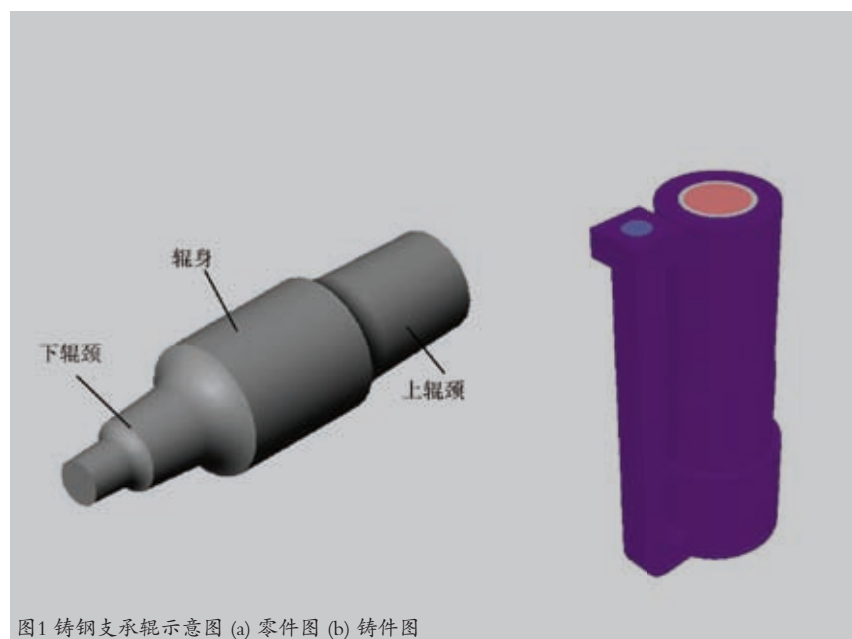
铸钢支承辊示意图 (a) 零件图 (b) 铸件图
